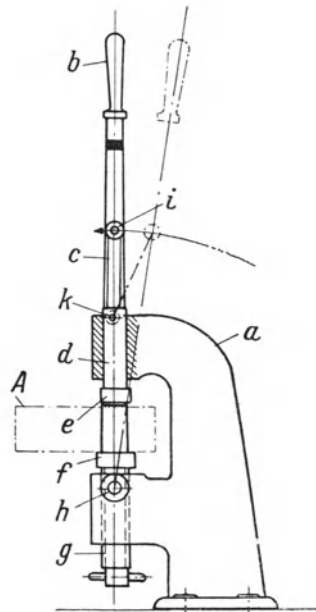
Vorrichtung zum Bezeichnen gerader Flächen mittels Kniehebeldruck.
